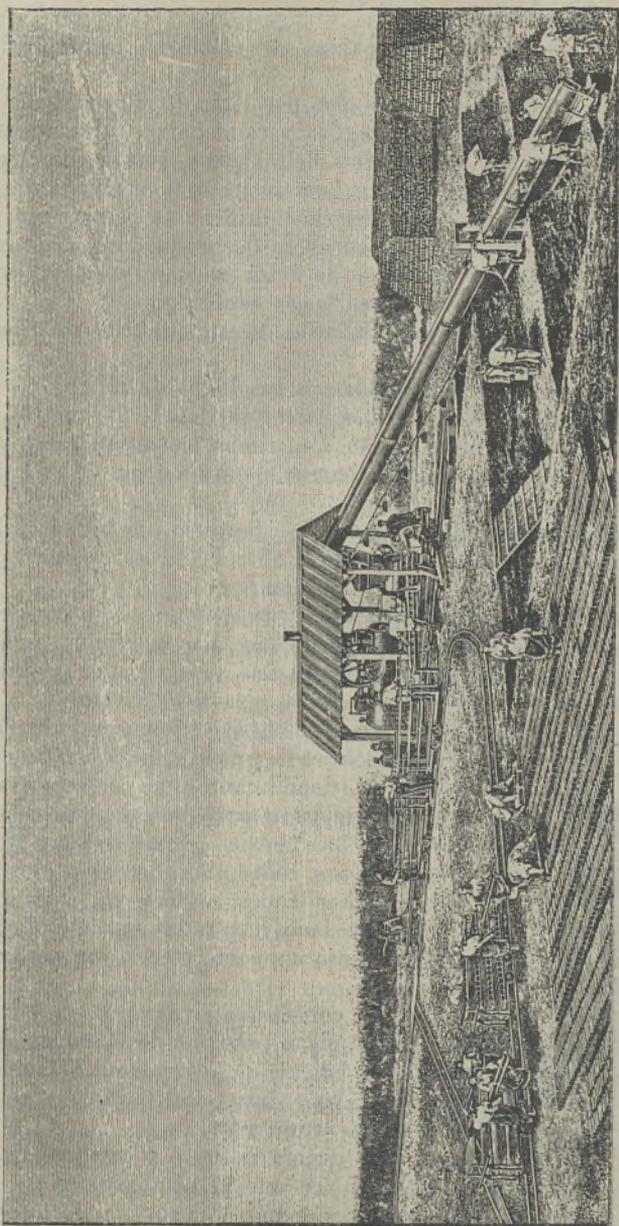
Fabrico mecanico de tijolo junto a uma barreira
